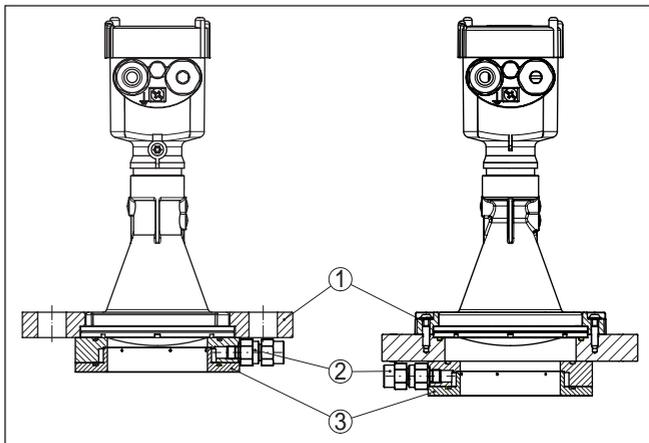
Conexão de limpeza no sensor de radar com flange de capa ou flange adaptador ASME 3"
